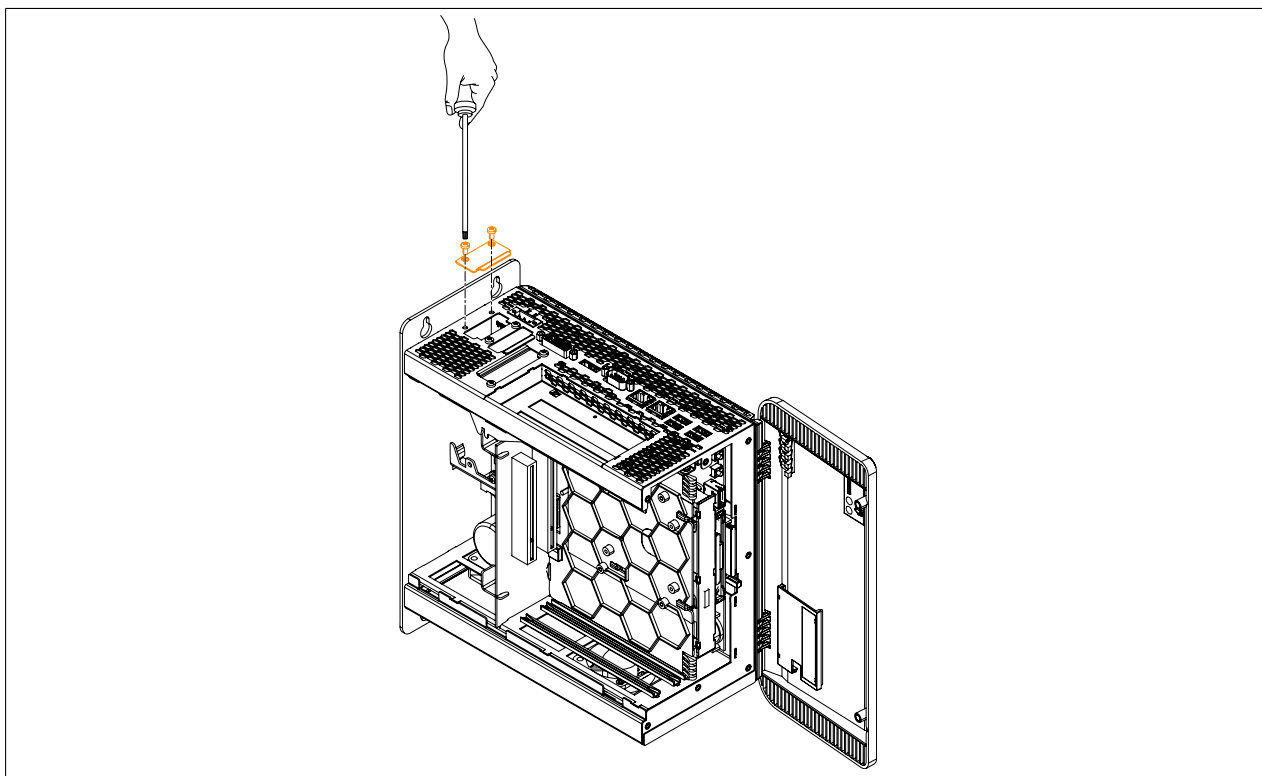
Kombitorxschrauben und Blindabdeckung entfernen
